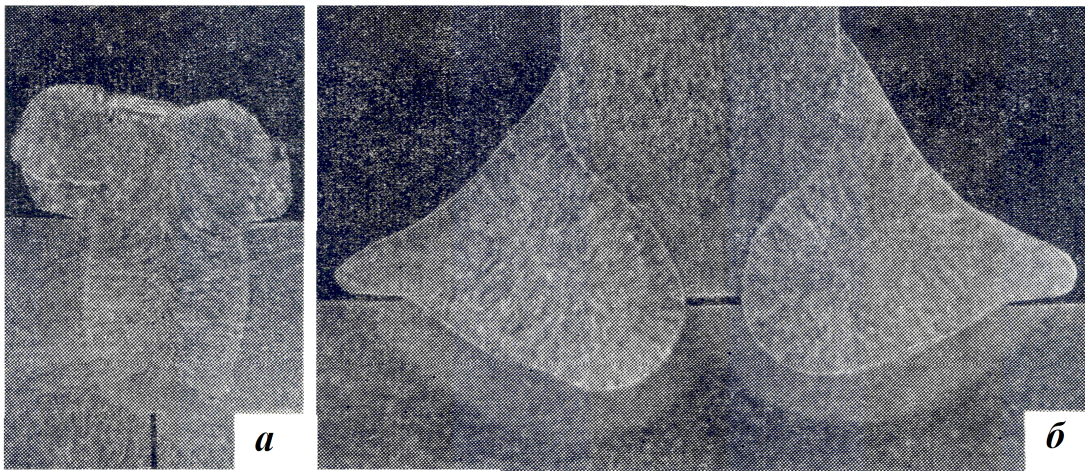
Наплав при сварке шва: *а* – стыкового; *б* – углового
